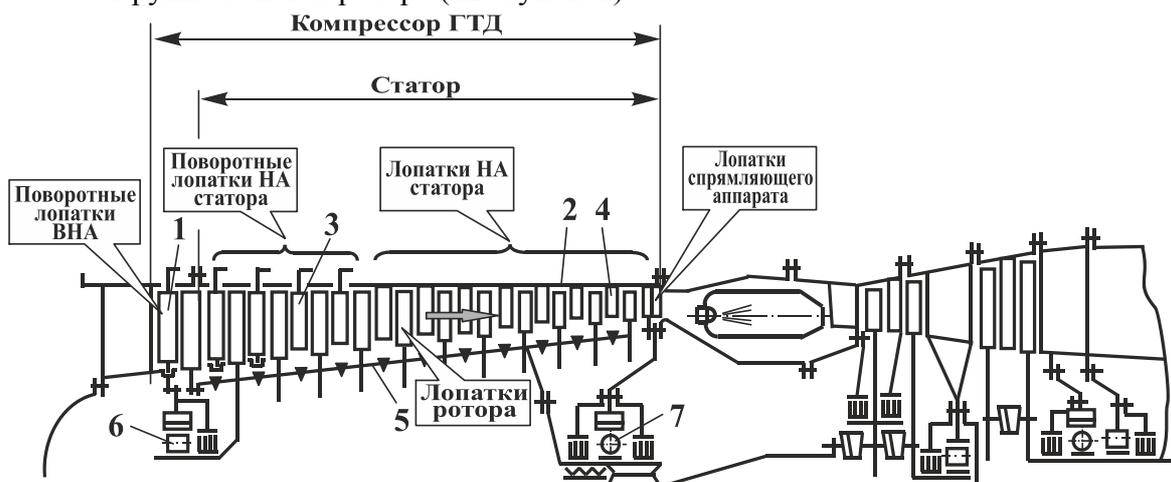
Конструктивная схема вертолетного ГТД модели ТВ3-117: 1 – поворотные лопатки входного направляющего аппарата (ВНА), 2 – статор компрессора, 3 – поворотные лопатки направляющего аппарата (НА) статора, 4 – лопатки НА статора, 5 – ротор компрессора, 6 – передняя радиальная опора, 7 – задняя радиально-упорная опора
